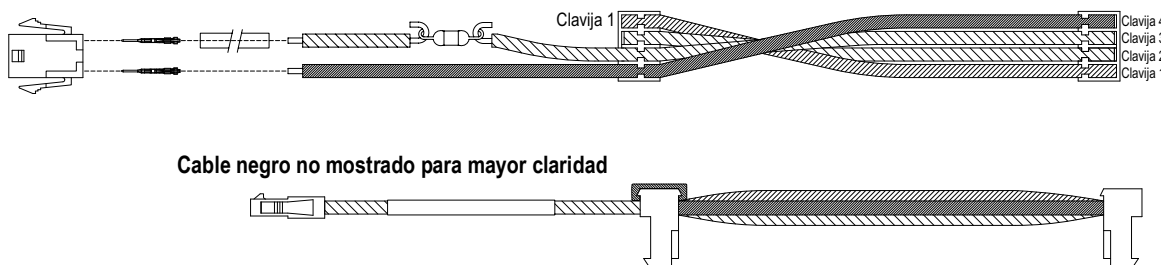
Cableado de retroadaptación para pantalla con retroiluminación LED y placa de la CPU verde
